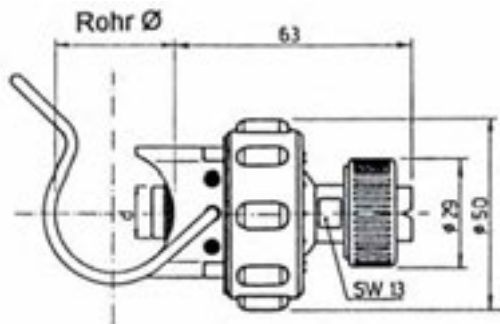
Abmessungen (Kugel = Ø 28,7 mm)
